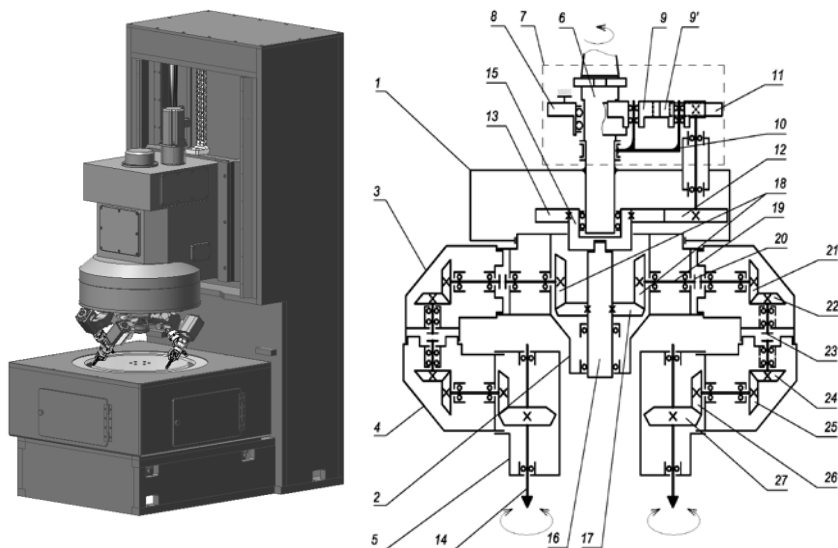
Модель станка для МАО концевой режущего инструмента и принципиальная схема рабочей головки
